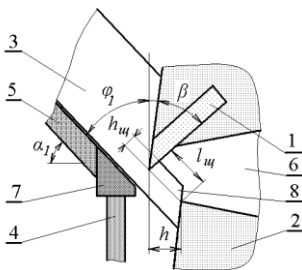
Общий вид рубильной машины и схема образования элементов щепы: 1 - нож; 2 - ножевой диск; 3 - измельчаемый материал; 4 - кожух; 5 - загрузочный патрон; 6 - подножевая щель; 7 - контрнож; 8 – щепка.
